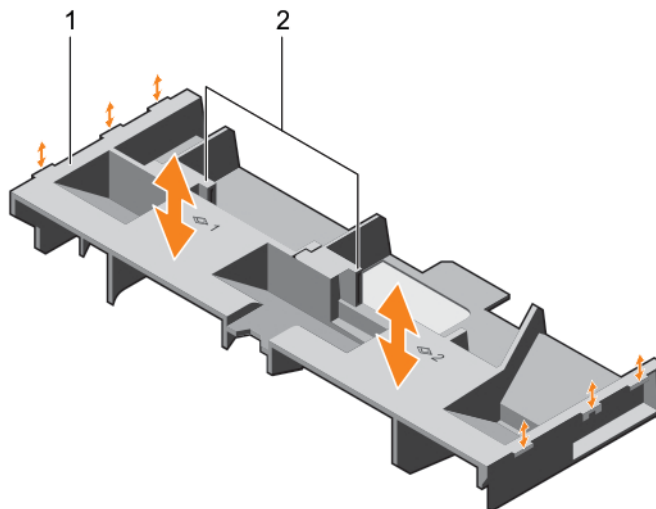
Extracción e instalación de la cubierta de refrigeración
